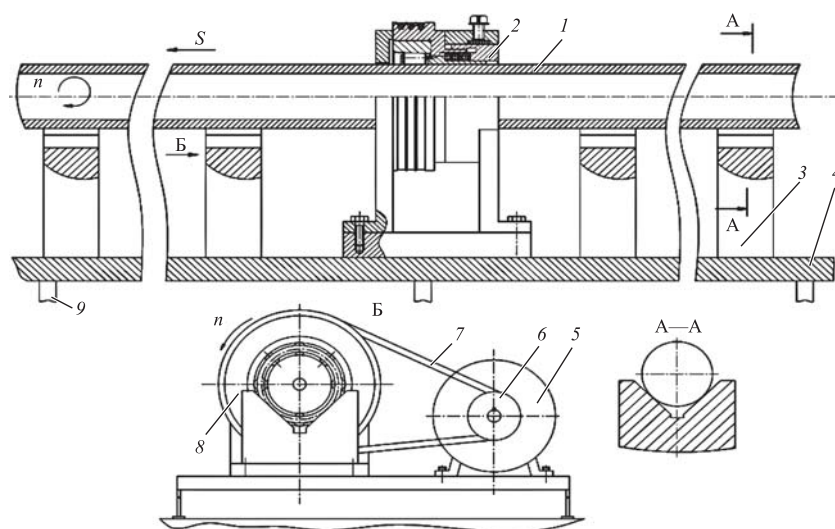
Схема устройства для обработки длинных валов и труб без применения токарно-винторезного станка:
